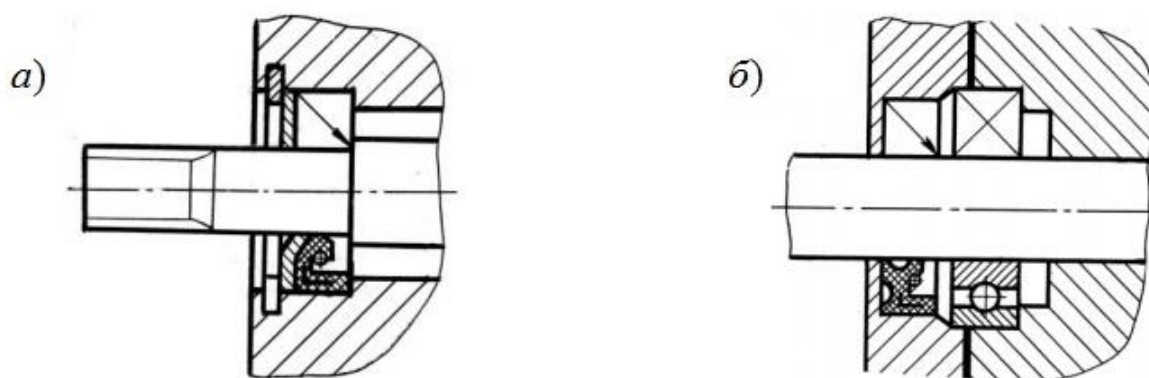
Изображение уплотнительных устройств и подшипников на сборочно чертеже
